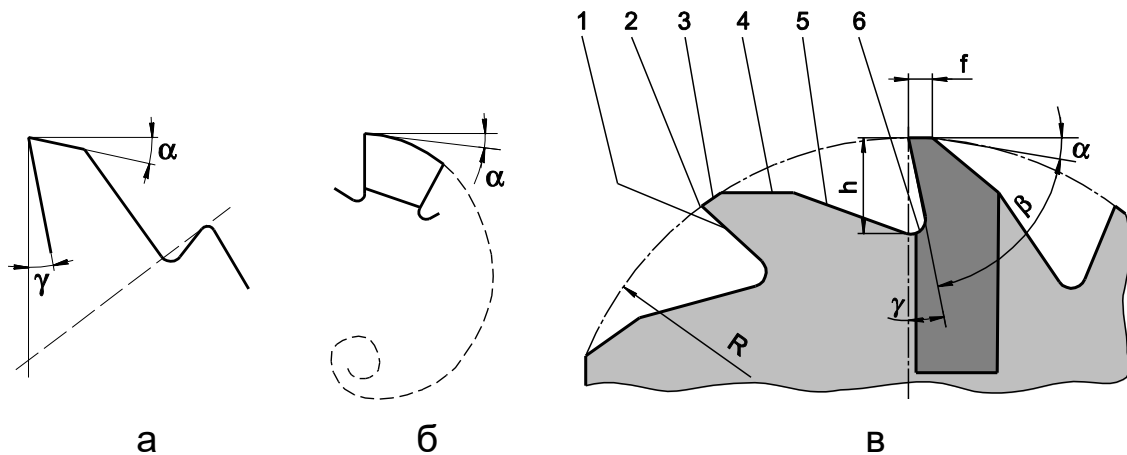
Элементы зуба фрезы: а, б – формы зубьев; в – сравнение элементов токарного резца и зуба фрезы
